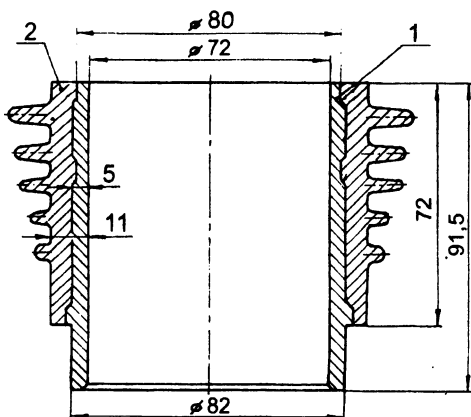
Биметаллический цилиндр пневмокомпрессоров трактора "Беларус" и автомобилей: 1 — чугунная вставка; 2 — алюминиевая рубашка
